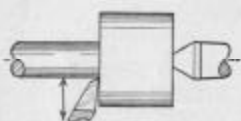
Emploi de l'Outil pour Surfacier à Gauche
